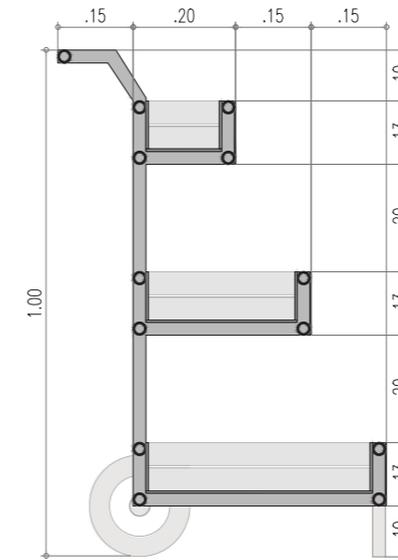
Sección puesto de venta ambulante tipo 2. Esc 1:15
